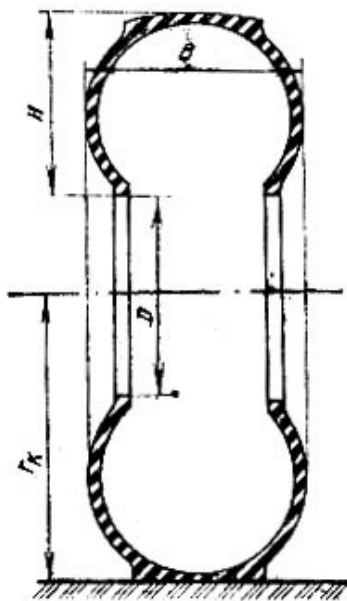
Основные геометрические размеры шины: D — посадочный диаметр; B — ширина профиля; H — высота профиля; r_k — радиус качения
